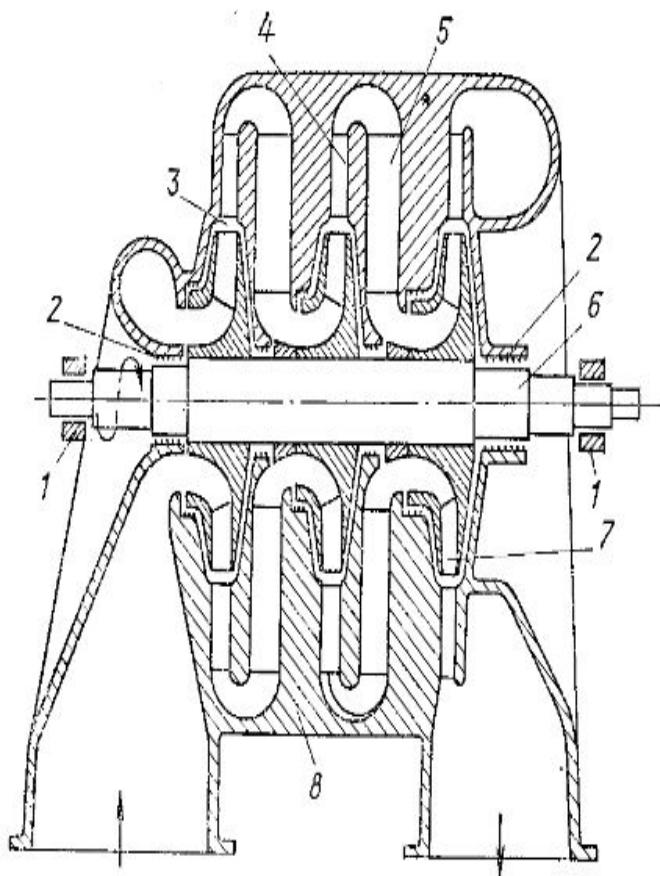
Схема многоступенчатого центробежного компрессора:
